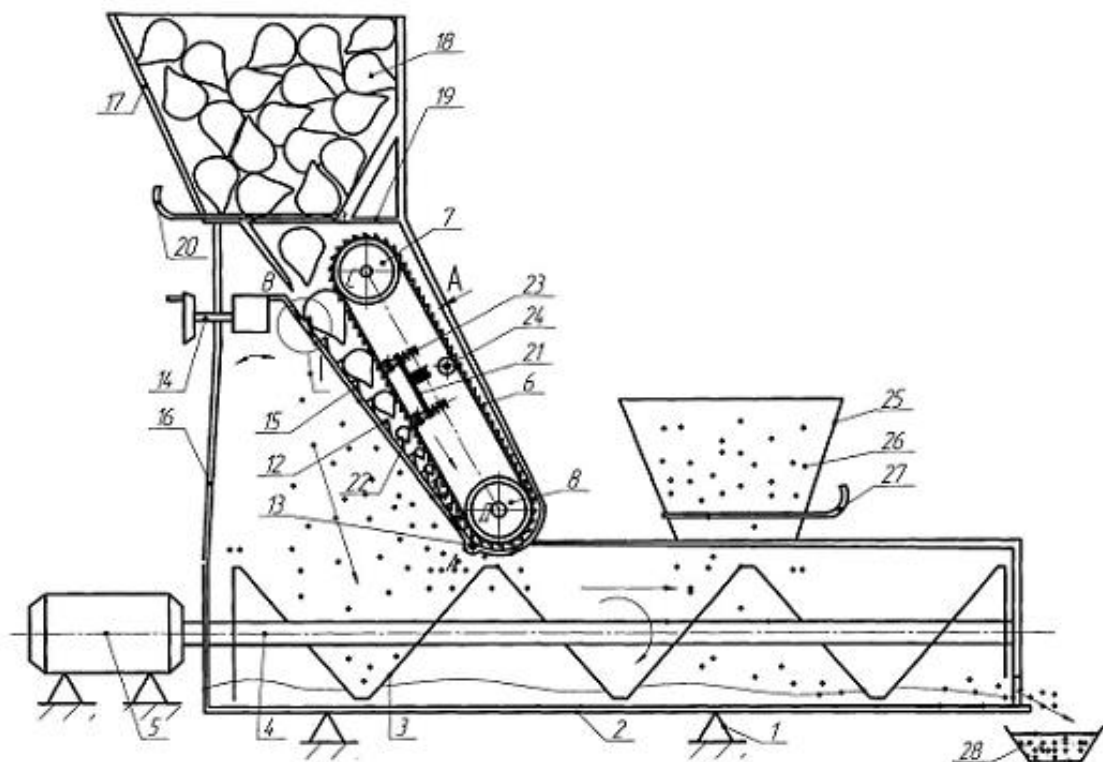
Конструктивна схема установки для подрібнення і змішування кормів
